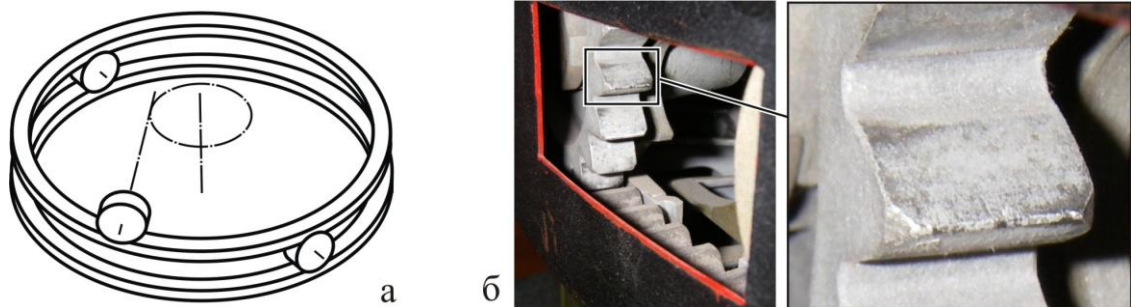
ОСКГП с плоскими колесами, изготовленными «приближенным» методом: а – схема механизма; б – передача со следами кромочного контакта на зубьях шестерни
